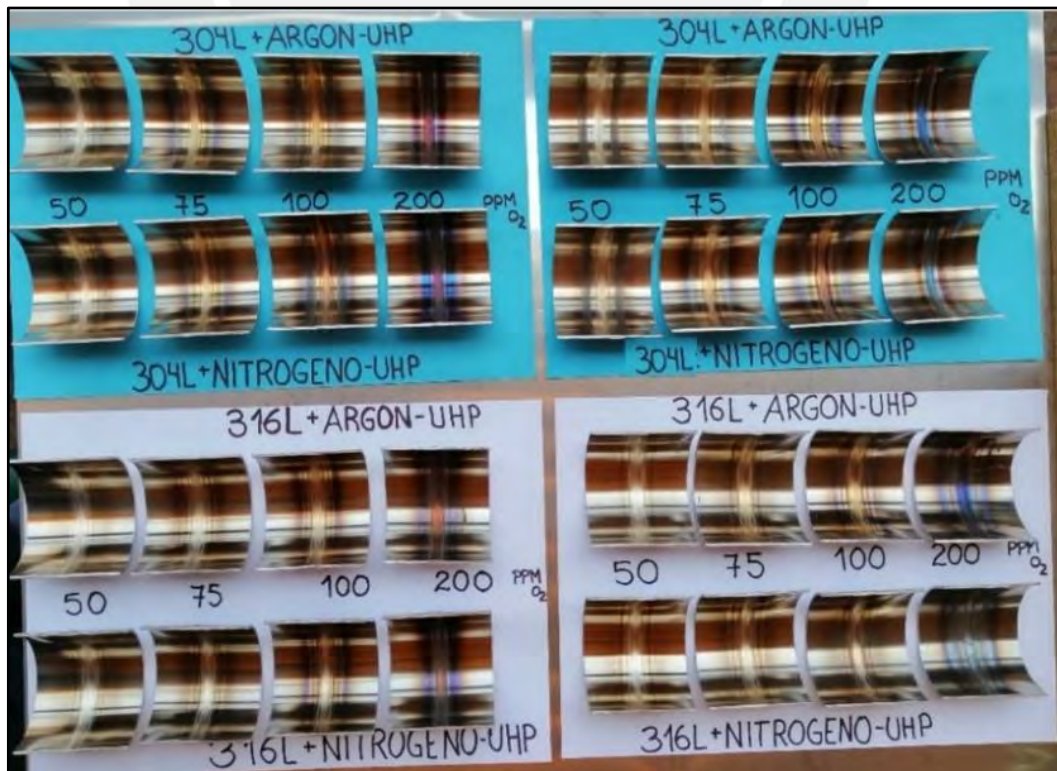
Clasificación de medias cañas por cada condición de soldadura.
